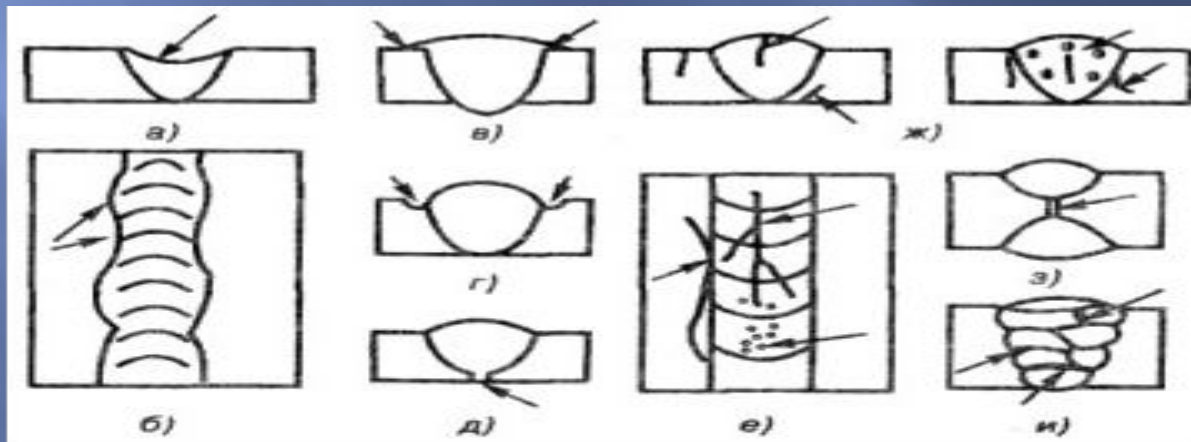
Виды дефектов сварных швов: а - ослабление шва б - неравномерность ширины, в - нащыв, г - подрез, с - непровар, с - трещины и поры, ж - внутренние трещины и поры, з - внутренний непровар, и - шлаковые включения
